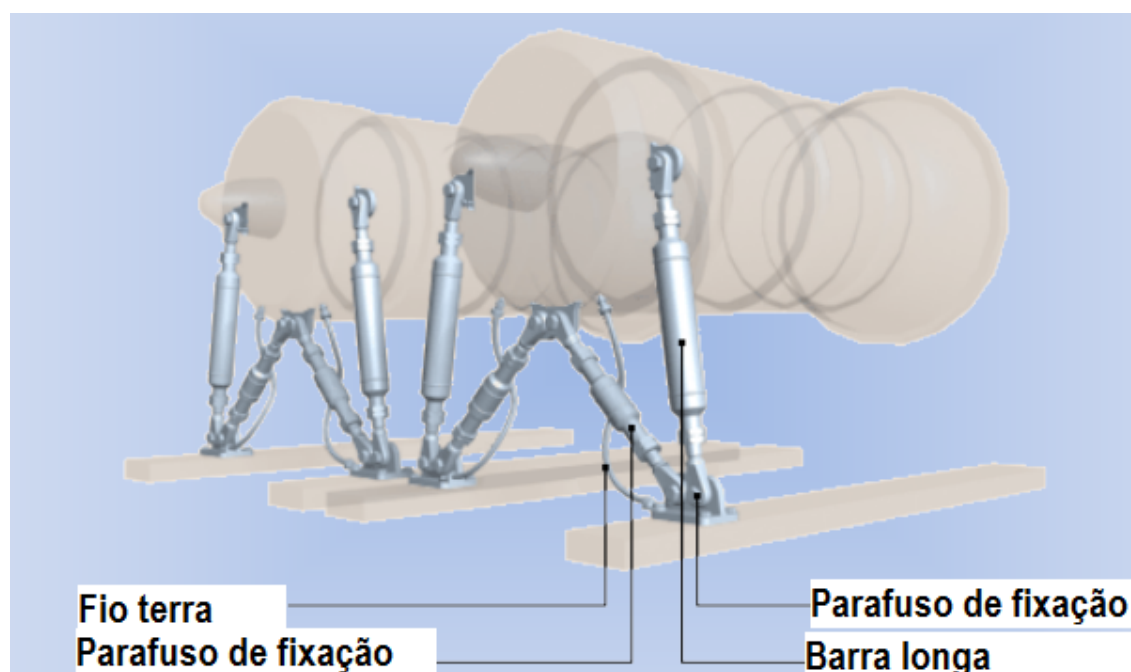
Fixação frontal do motor TV3-117VM.
